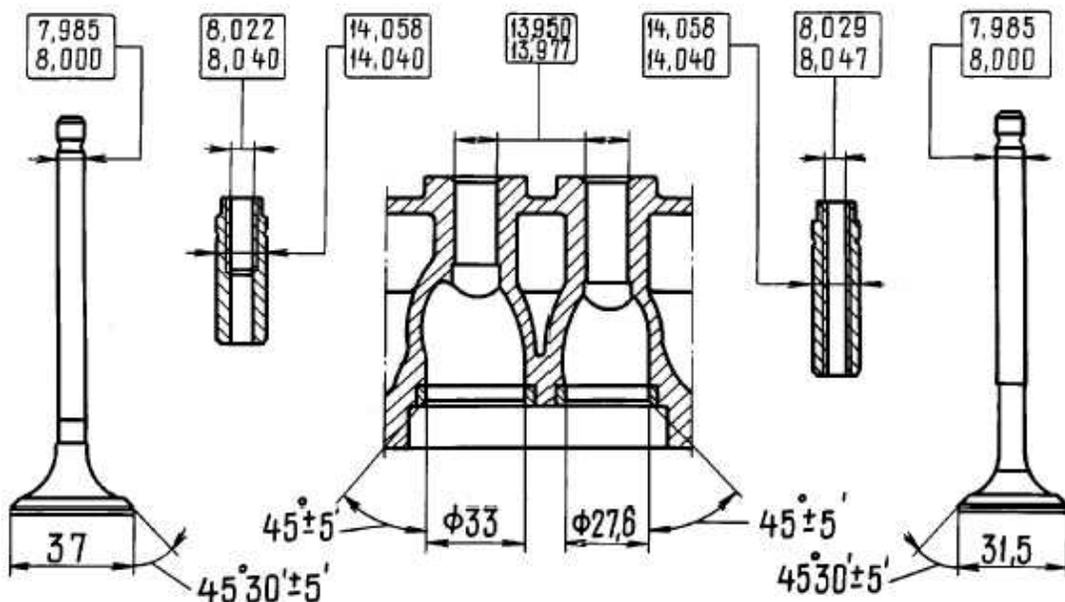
Dimensiones principales de la culata de los cilindros, válvulas y casquillos guía
